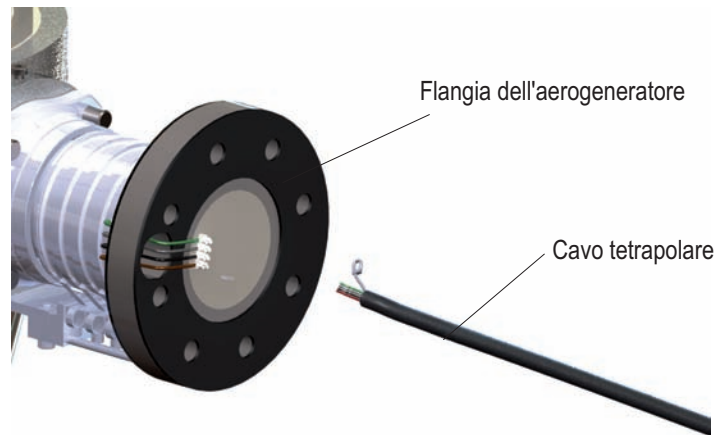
Dettaglio del collegamento del cavo di potenza.
